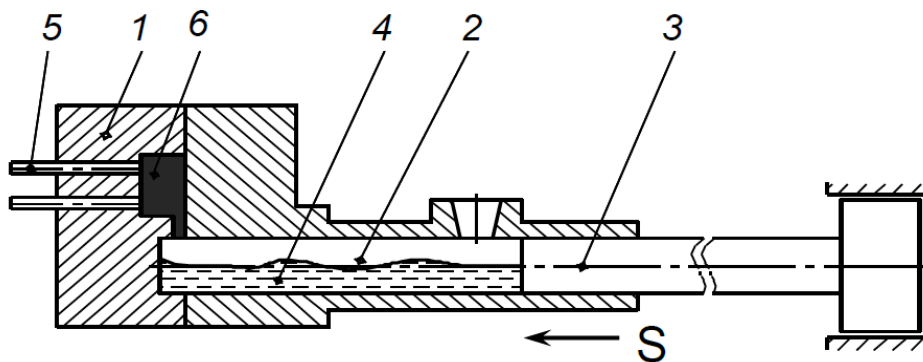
Условная схема холодной горизонтальной камеры прессования: 1 – пресс-форма; 2 – камера прессования; 3 – поршень; 4 – расплав; 5 – выталкиватели отливок; 6 – отливка
